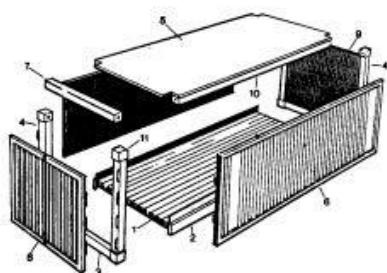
Vista detallada del diseño y de la construcción del contenedor
